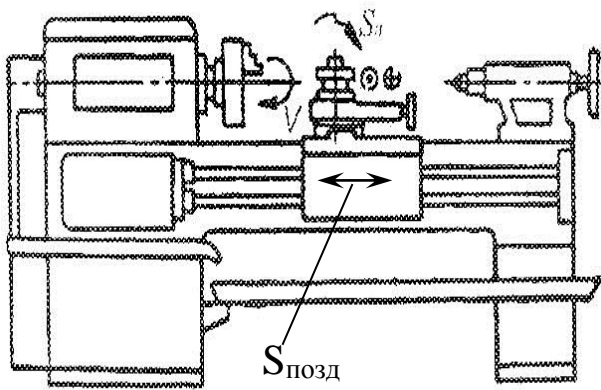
Загальний вид токарно-гвинторізного верстата
